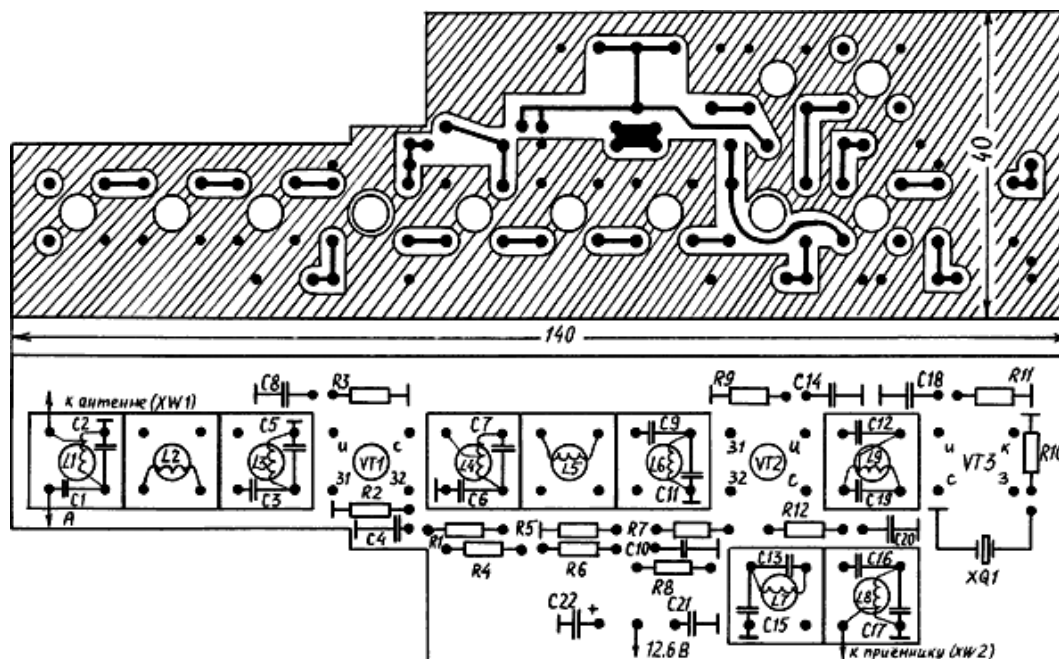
Эскизы монтажной платы конвертера и расположения деталей на ней
